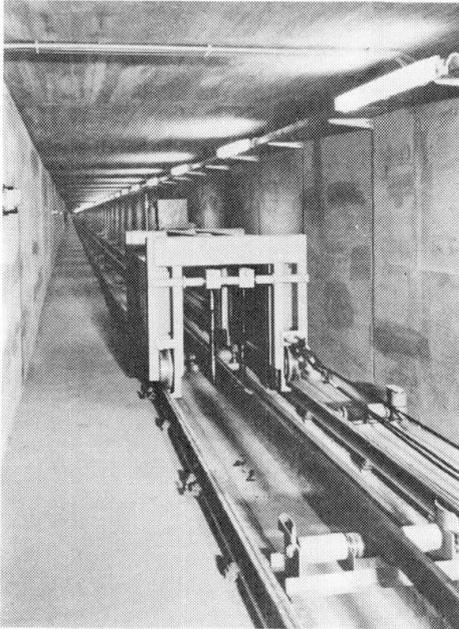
Seilreckanlage, 400 m lang, mit Einziehwagen, Kuppelwagen im rückwärtigen Teil des Tunnels
